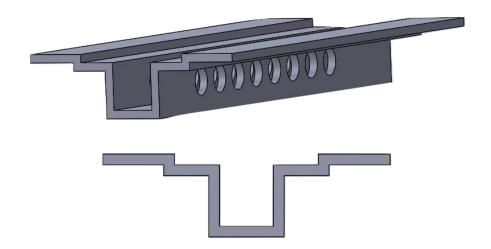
Detalle base sistema empuñadura Fuente: Elaboración Propia
